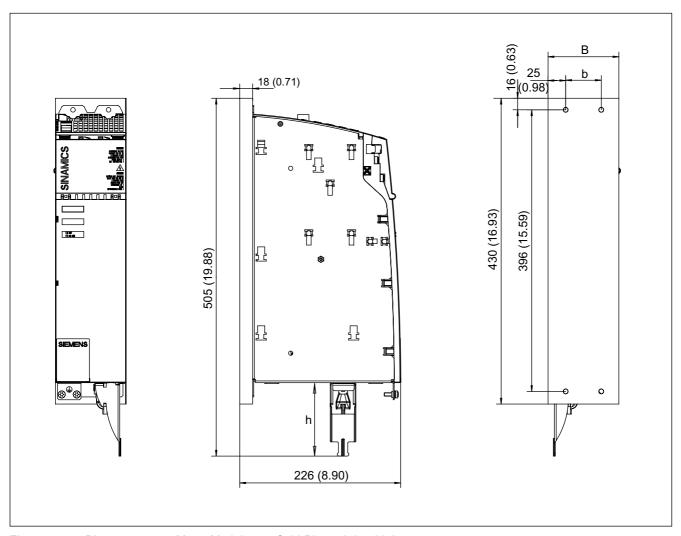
Disegno quotato Motor Module con Cold-Plate 18 A e 30 A
